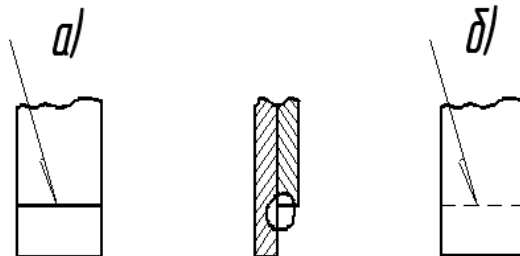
Условные изображения сварных швов на чертежах
